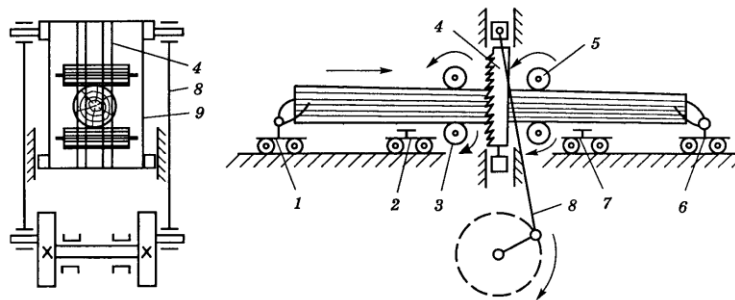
Принципова схема одноповерхової пилорами: 1 – основний подавальний візок; 2 – підтримуючий візок; 3 – передні вальці; 4 – пилкова рама; 5 – задні вальці; 6, 7 – з'єднані візки; 8 – шатун; 9 – стійки пилкової рами
